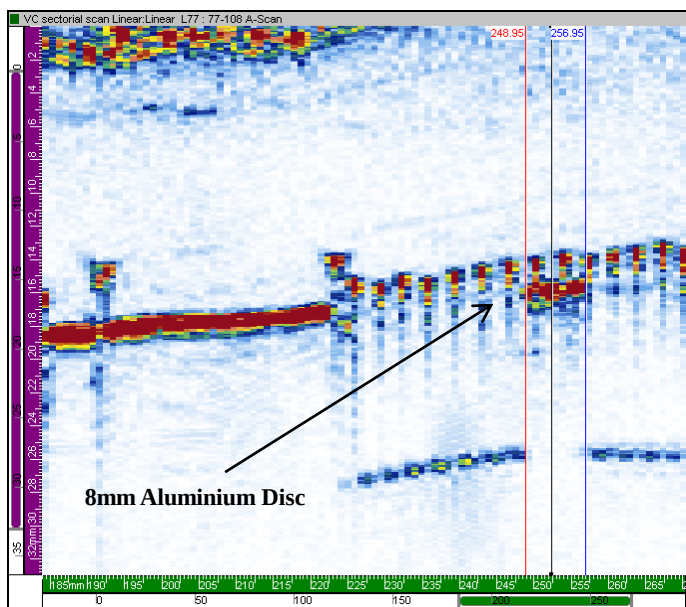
IMAGEN DE UNA UNIÓN POR EF EN TUBO DE PE DE 180MM CON UN DISCO DE ALUMINIO DE 8mm
